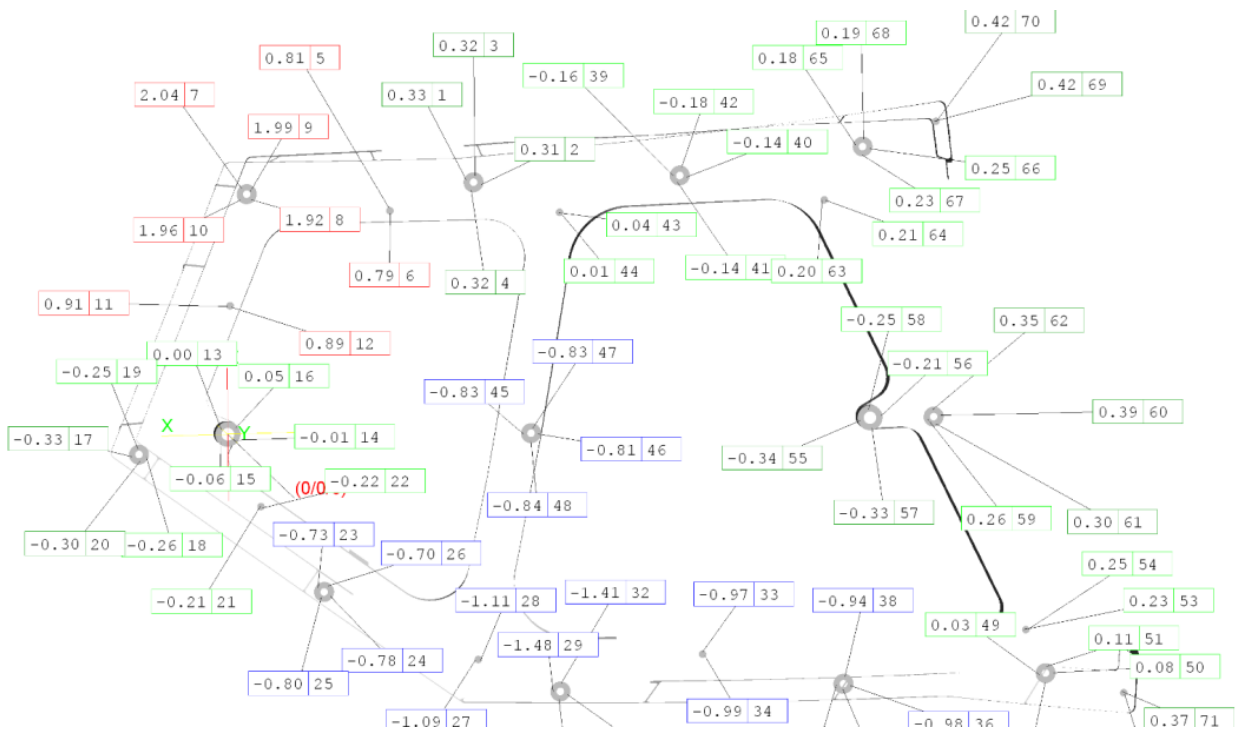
Результаты измерения коробления новой заготовки с равномерным припуском
